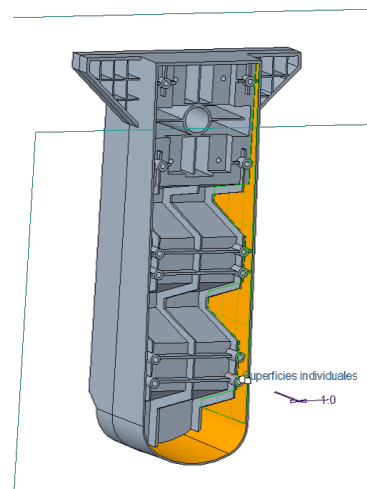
Ángulo de desmoldeo trasero.
